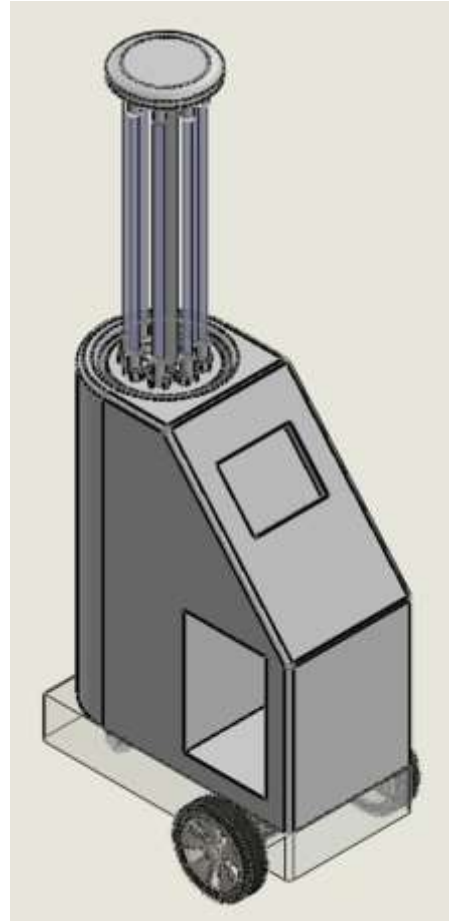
Ensamblaje final en CAD del robot desinfectante.
